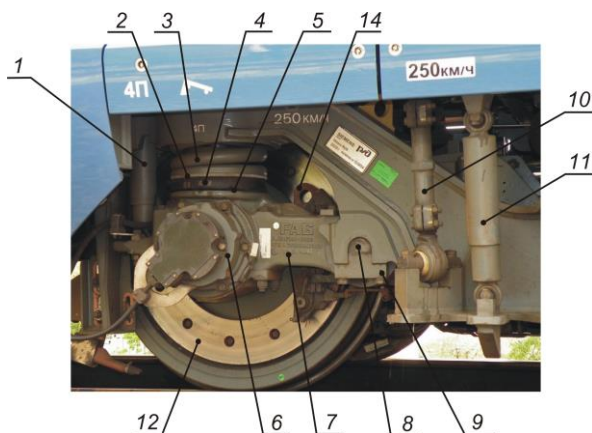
Колесная пара с элементами первой ступени рессорного подвешивания тележки ВСП «Сапсан»:
